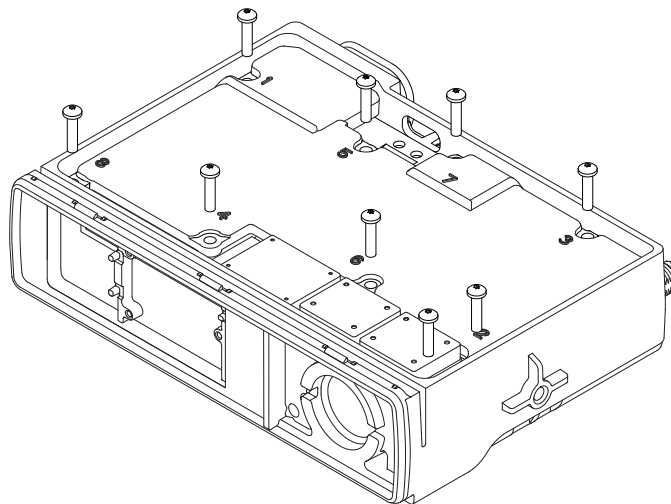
Druckguss-Hauptabdeckung an Chassis anbringen
